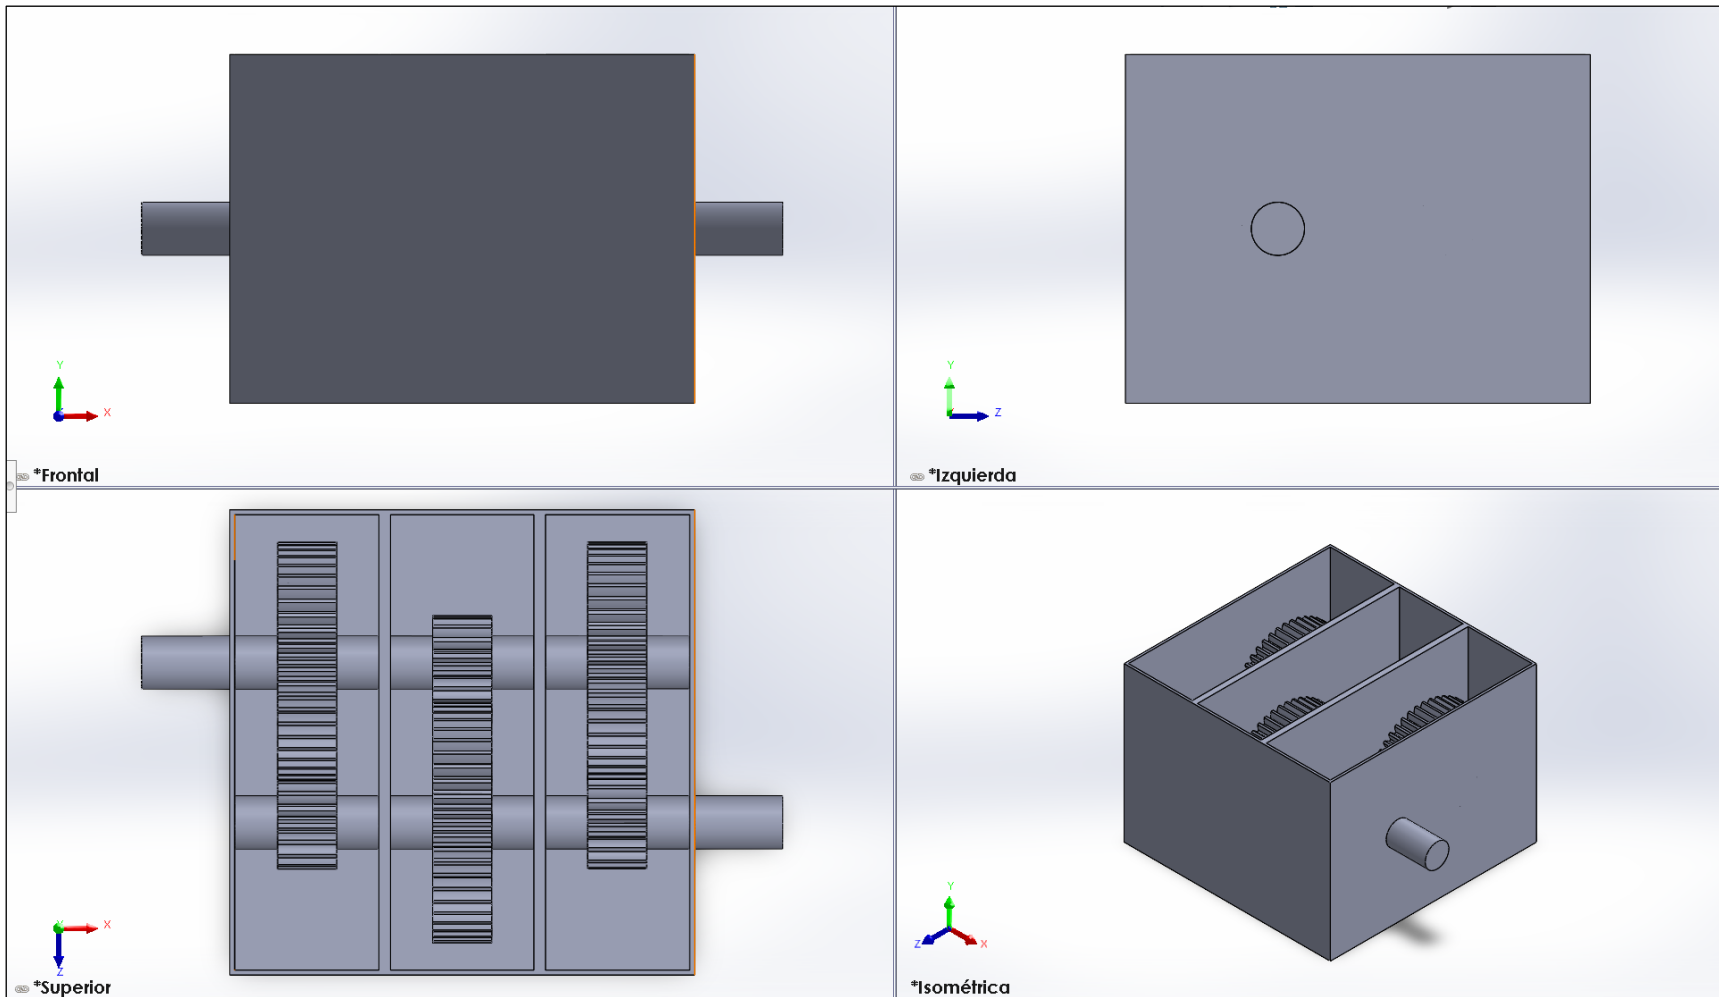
Ensamblaje de la caja reductora de velocidad con engranajes de dientes rectos.
